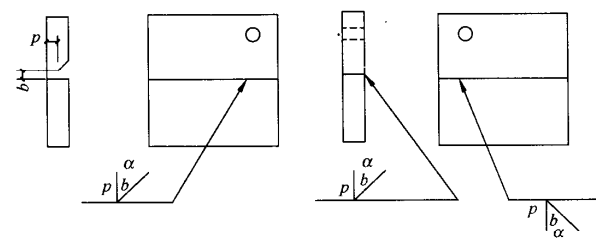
一个焊件带坡口的焊缝标注方法
